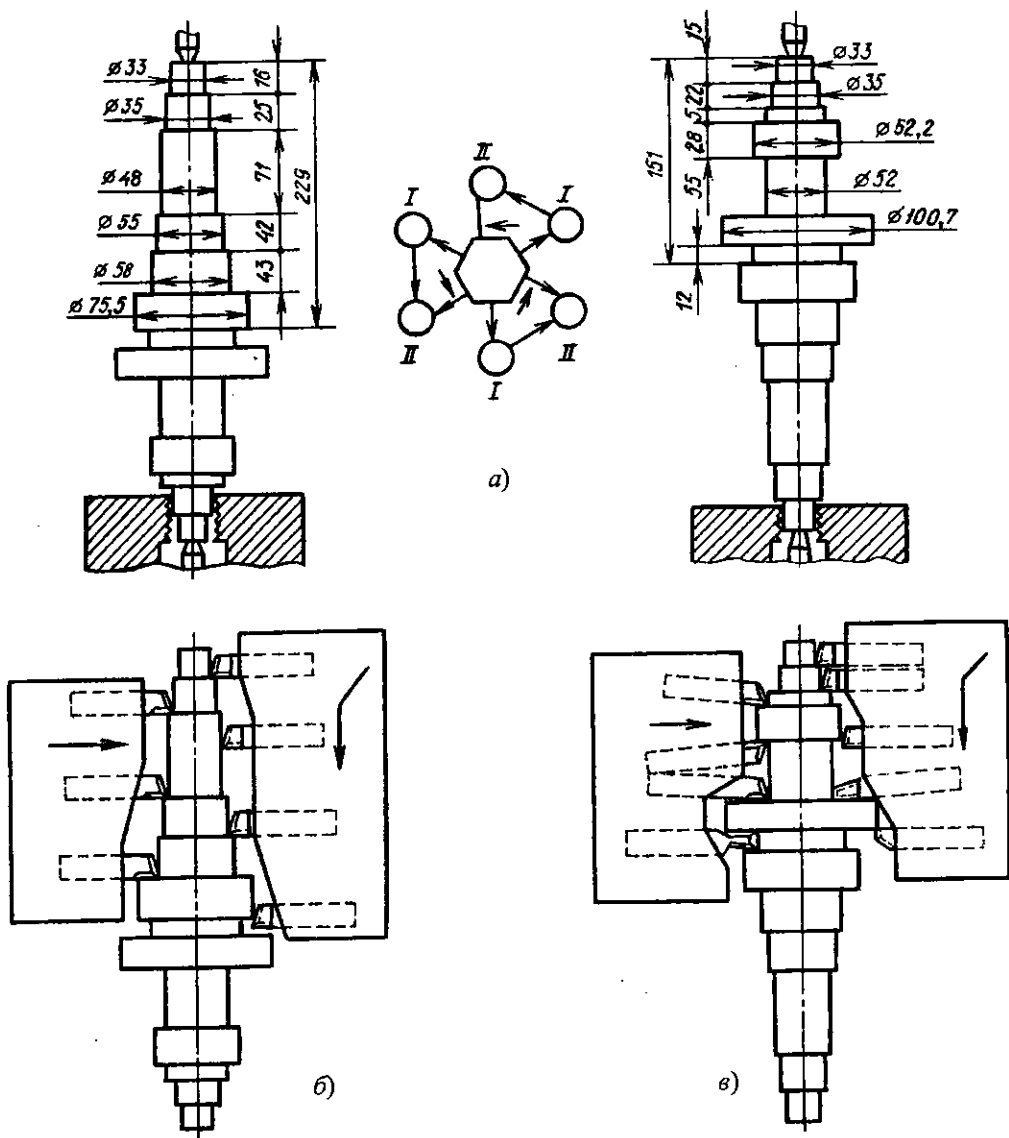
Схема обработки детали на вертикальном многошпиндельном полуавтомате параллельного действия для двухциклового обработки ступенчатого валика: а – схема расположения позиций полуавтомата; б – обработка валика с одной стороны; в – обработка валика с другой стороны
